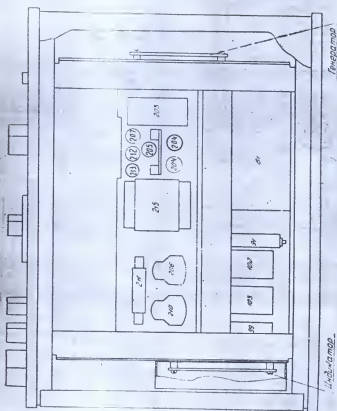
Универсальный мост Е7-4 (вид сверху)
